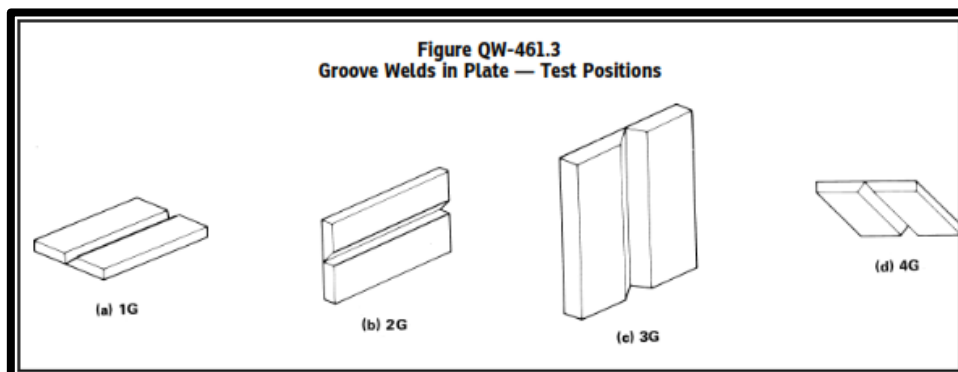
QW-461.3 Soldaduras de ranura en planchas – posiciones de ensayos. Tomada del estándar ASME sección IX
